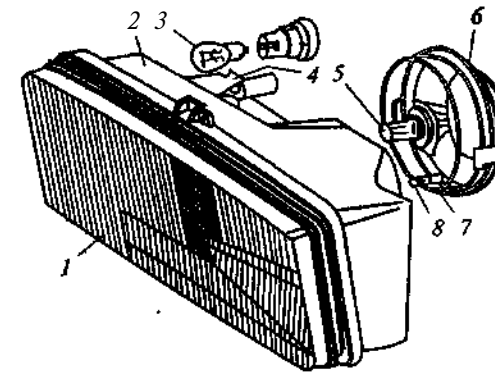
Блок-фара автомобиля ВАЗ-2105: 1 — рассеиватель; 2 — корпус; 3 — лампа указателя поворота; 4 — скоба для крепления; 5 — галогенная лампа основного света; 6 — кожух; 7 — уплотнитель; 8 — лампа габаритного света
